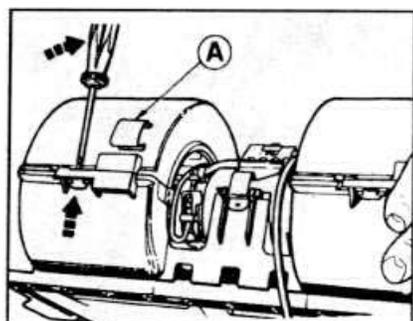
Расположение скобы крепления (А) кожуха вентилятора и отжатие фиксирующего язычка отверткой.
